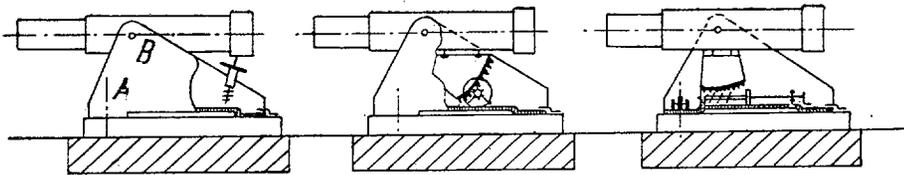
ª.—Ejemplos de mecanismos de puntería en altura: izquierda, mecanismo de husillo; centro, mecanismo de piñón y sector dentado; derecha, mecanismo de tornillo sin fin.
